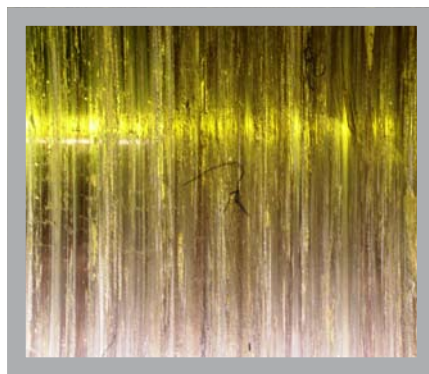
Вид поверхности подшипника скольжения при износе схватыванием второго рода
